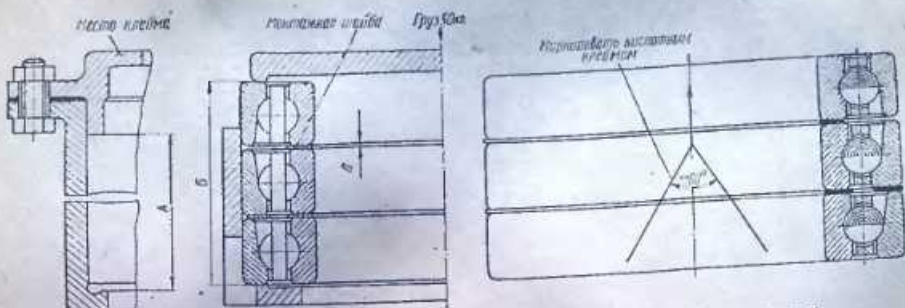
Схема приложения нагрузки на подшипники фланца вала при подборе регулировочной шайбы
